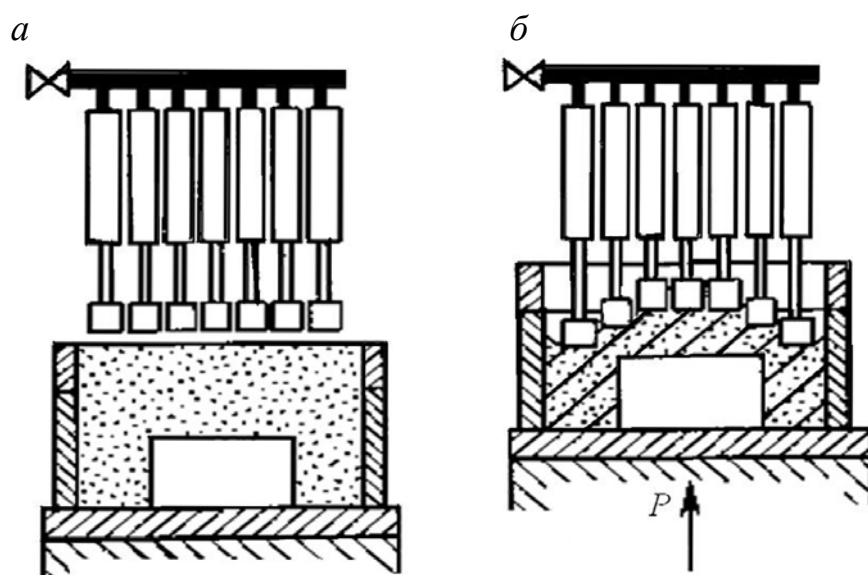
Принцип работы пассивной многоплунжерной прессовой головки
